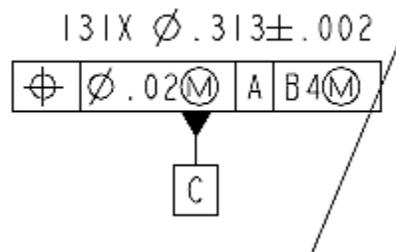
Tolerancia de posición de los barrenos.
